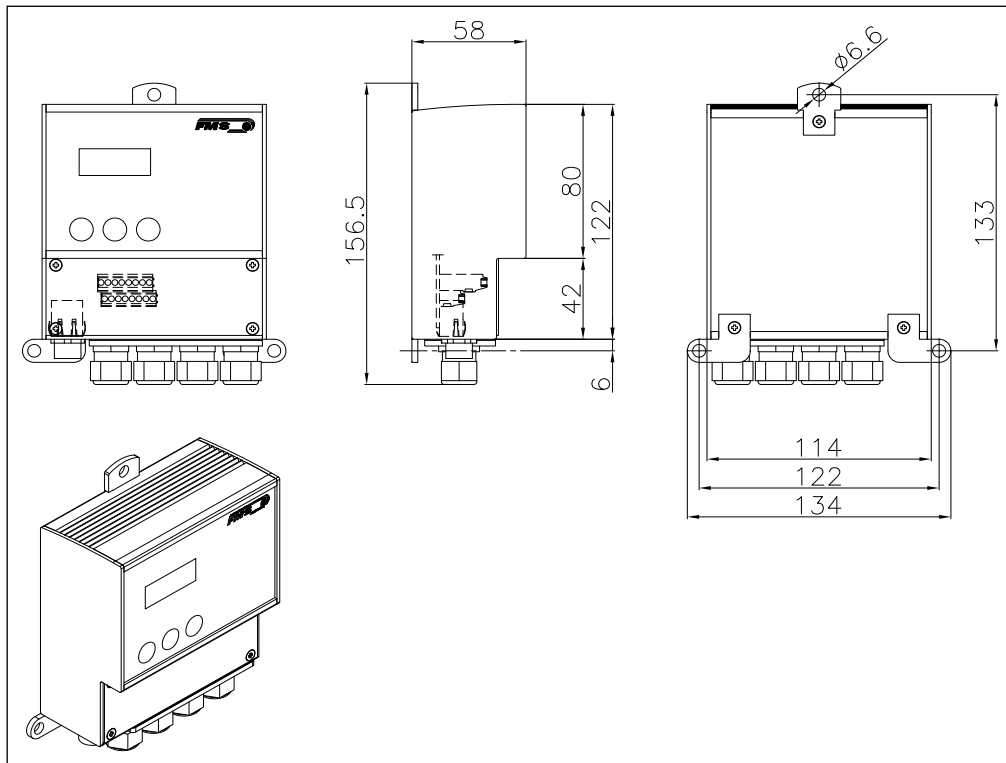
Aussenabmessungen EMGZ309.W Wandmontage
